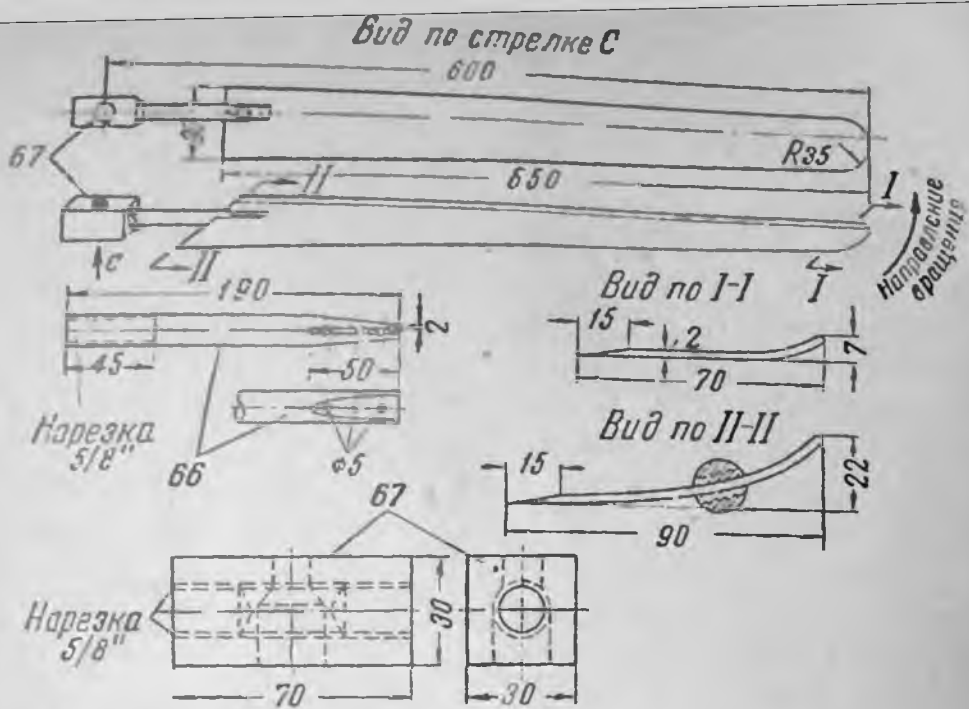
Металлическое крыло ветроколеса УД-1.6 и его детали:
